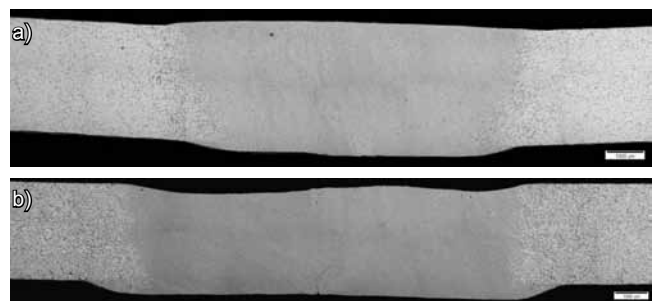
Makrostruktura złączy zgrzewanych metodą FSW: a) AZ91, 560 obr/min, 224 mm/min; b) AM-Lite, 355 obr/min, 224 mm/min
